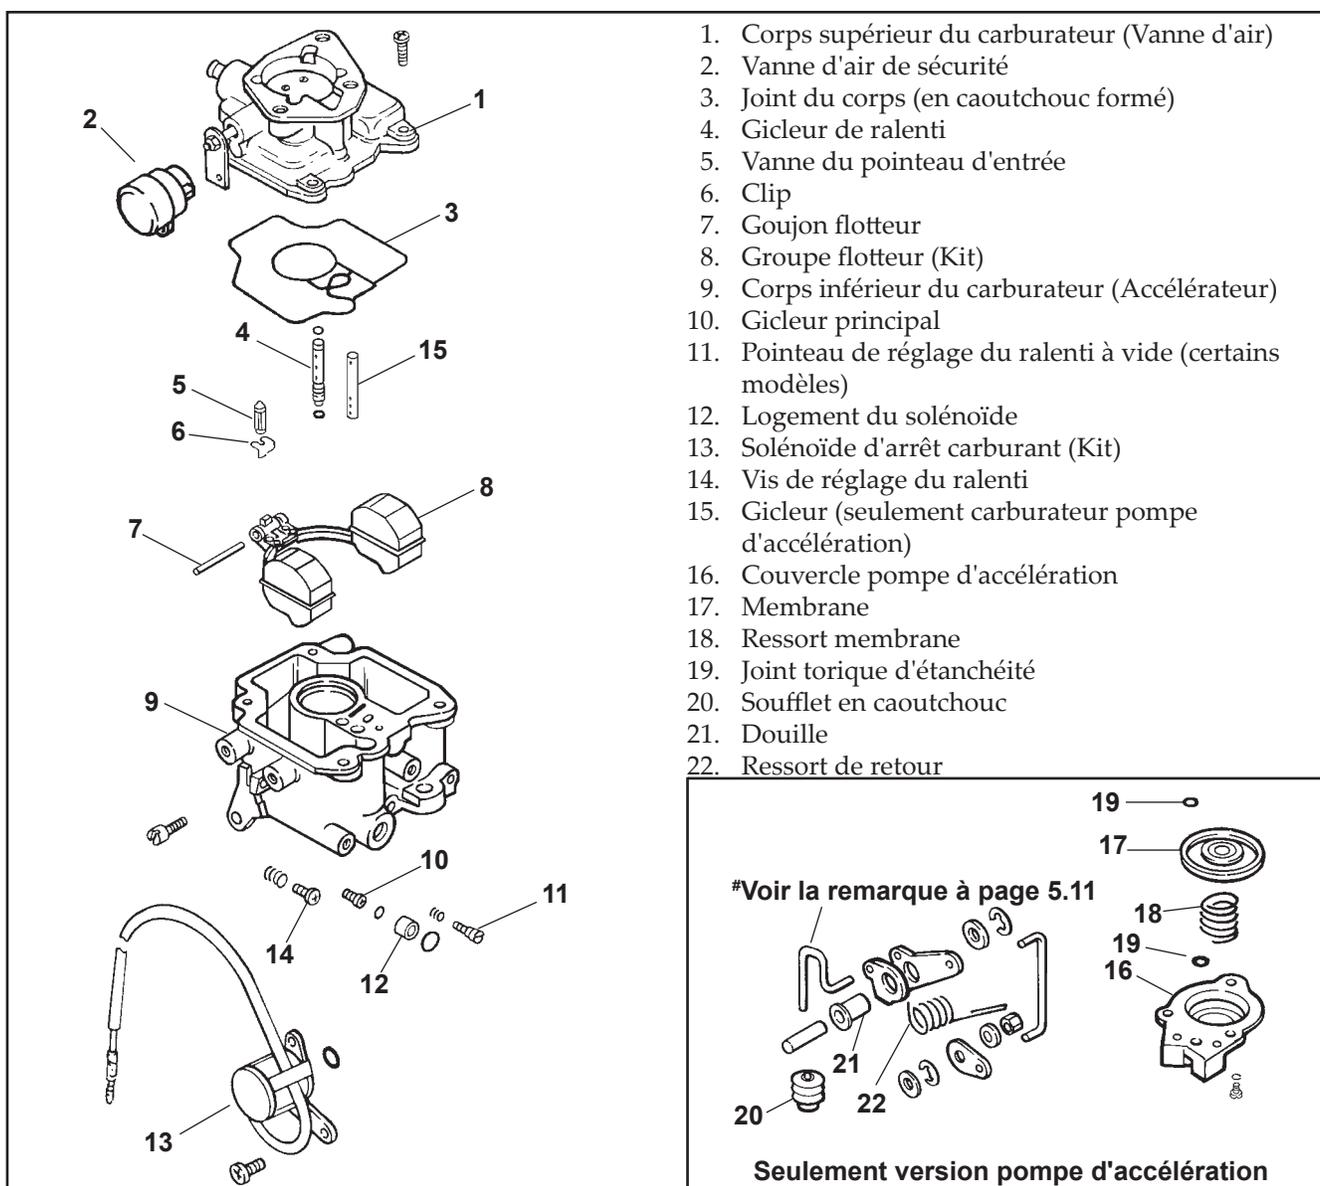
Carburateur CH18-740 – Vue éclatée.
